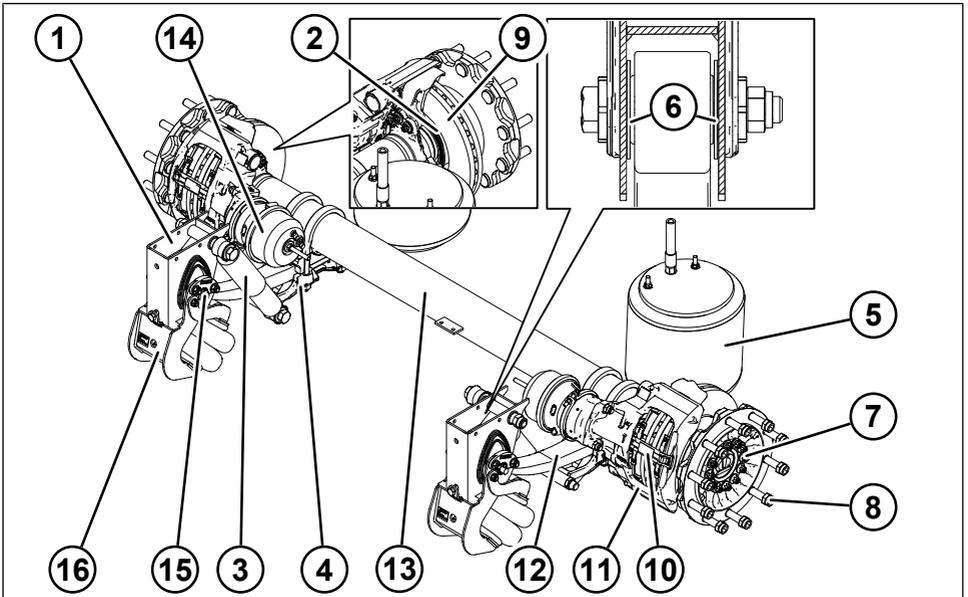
Vue d'ensemble de la maintenance (bras de suspension pneumatique inférieur)
